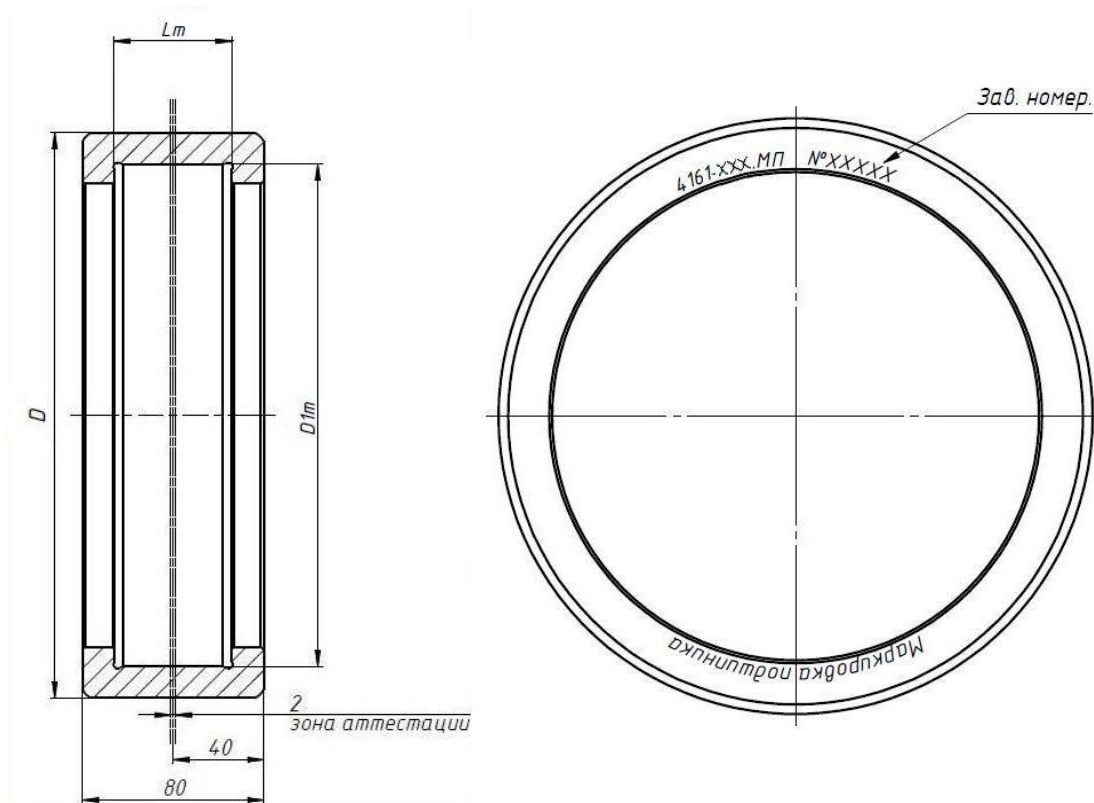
Эскиз мер для поверки приборов модели 4161 с обозначением основных размеров
